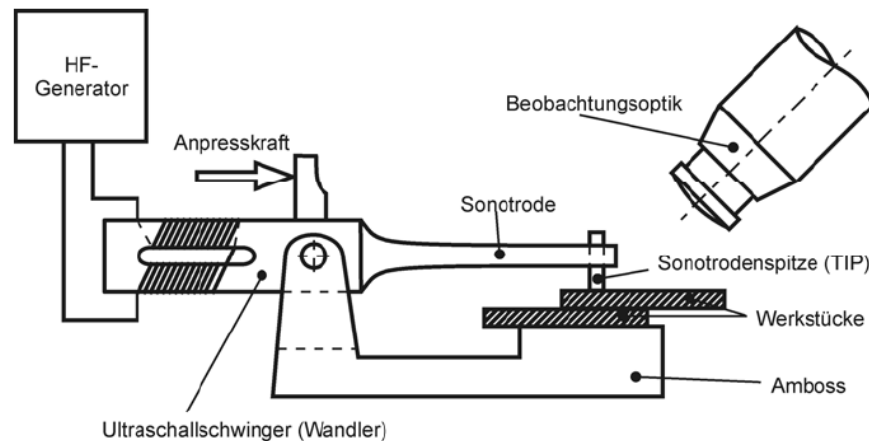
Schema Ultraschallschweißen [28]
